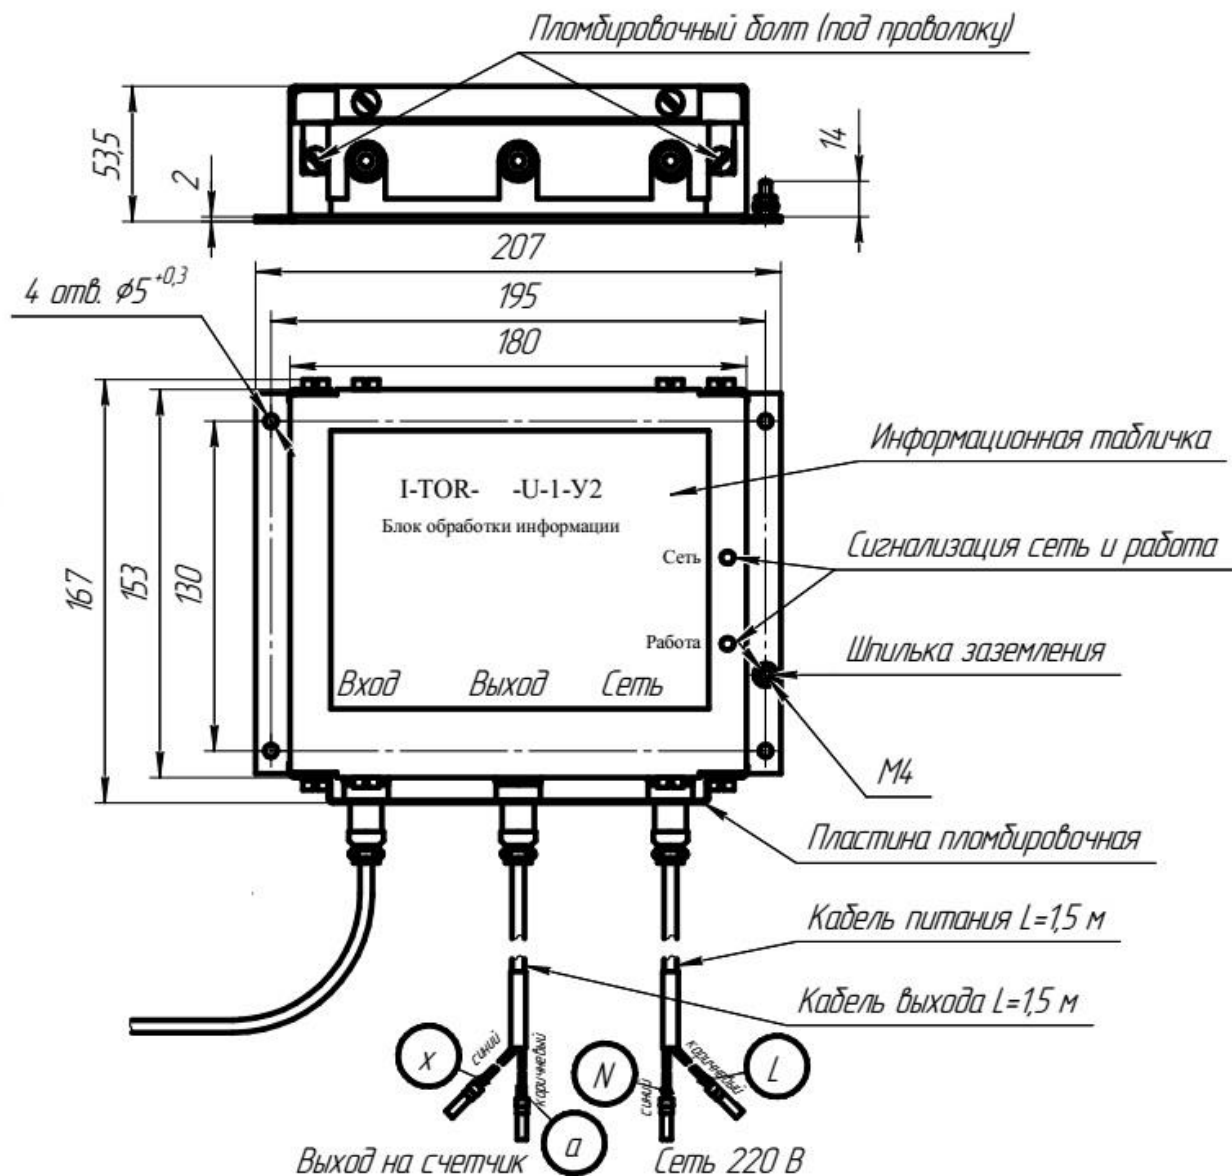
Габаритно-присоединительные размеры блока обработки информации устройства I-TOR, схема выполнения соединений
